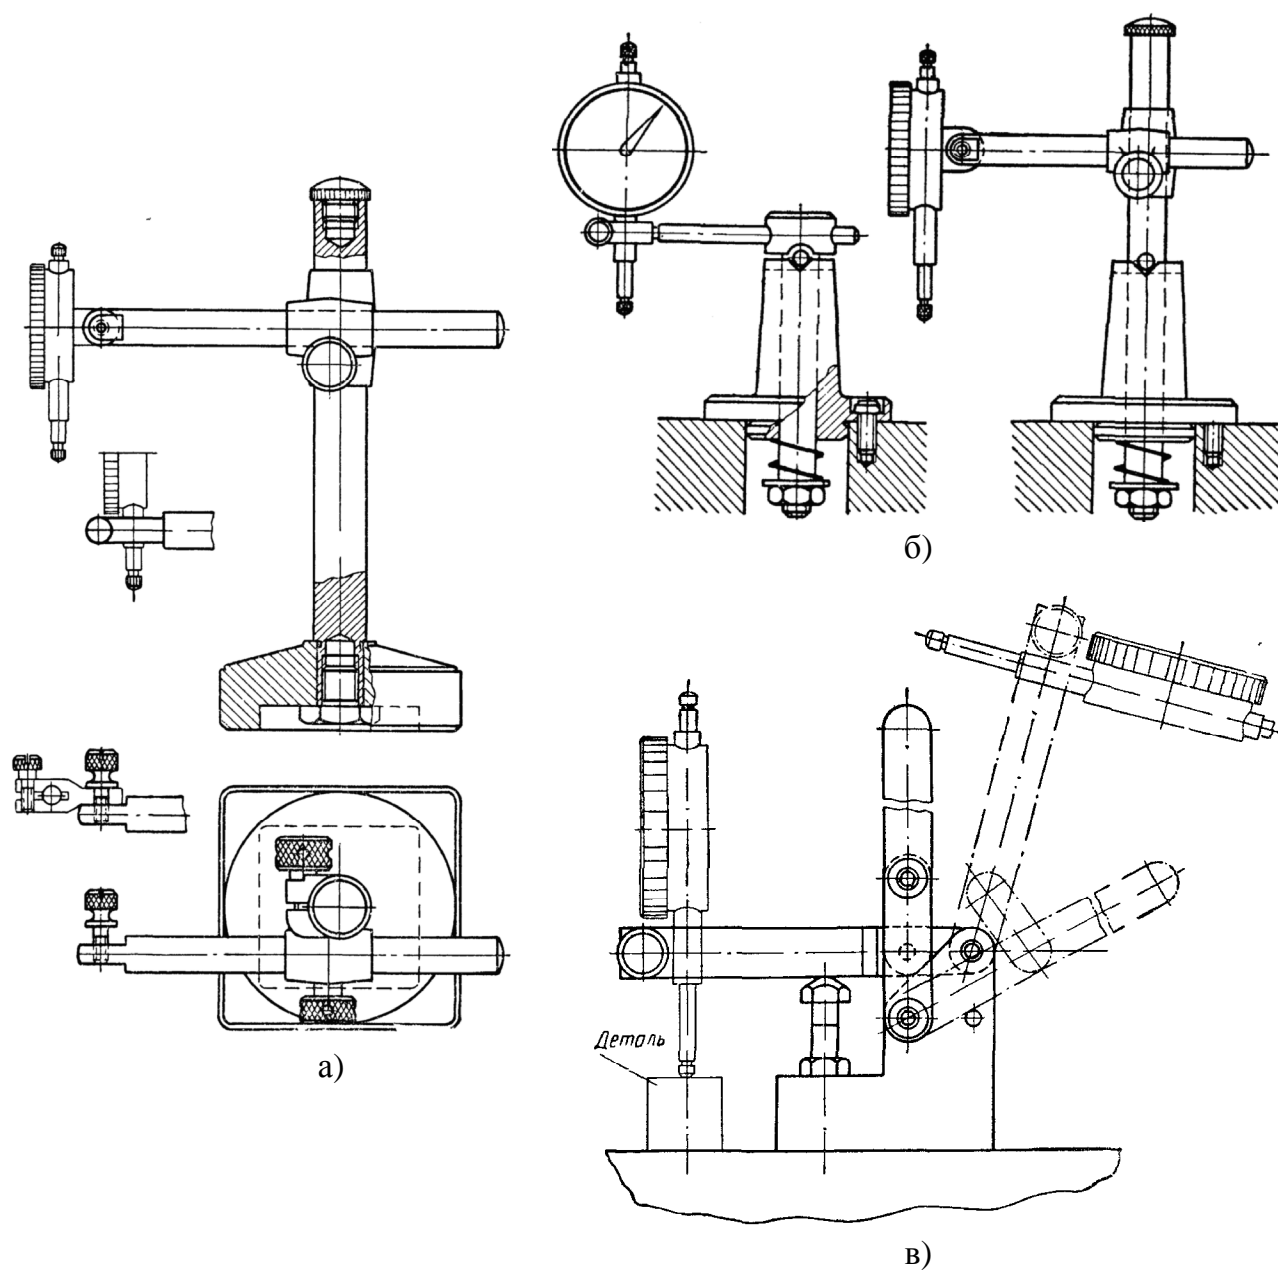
Варианты конструкции штативов для установки индикаторов и измерительных головок: универсальный штатив для индикатора (а), поворотный штатив (б), откидной штатив (в)
